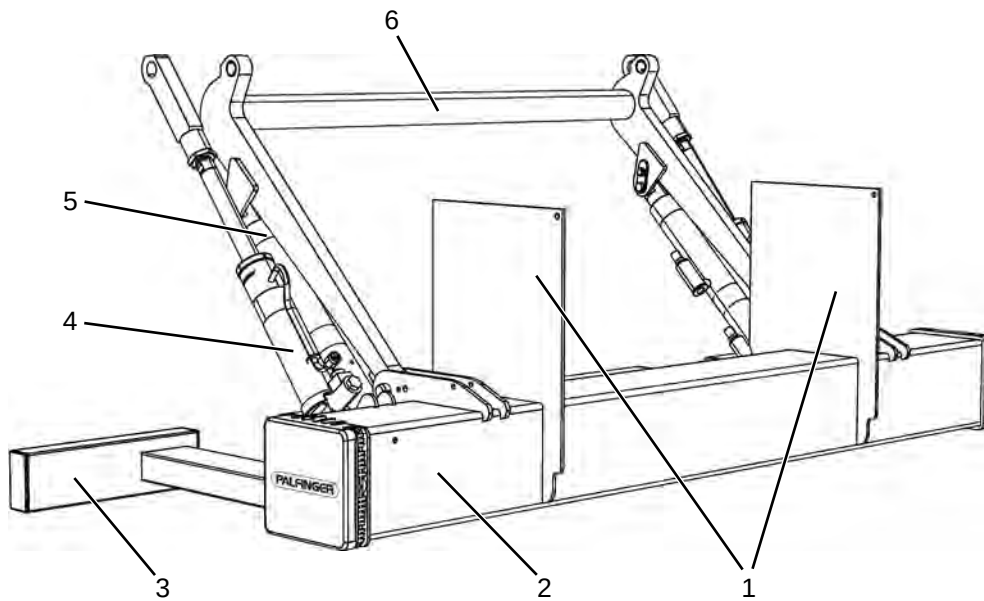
Hubladebühne mit Schweißkonsolen und Einschubaggregat
